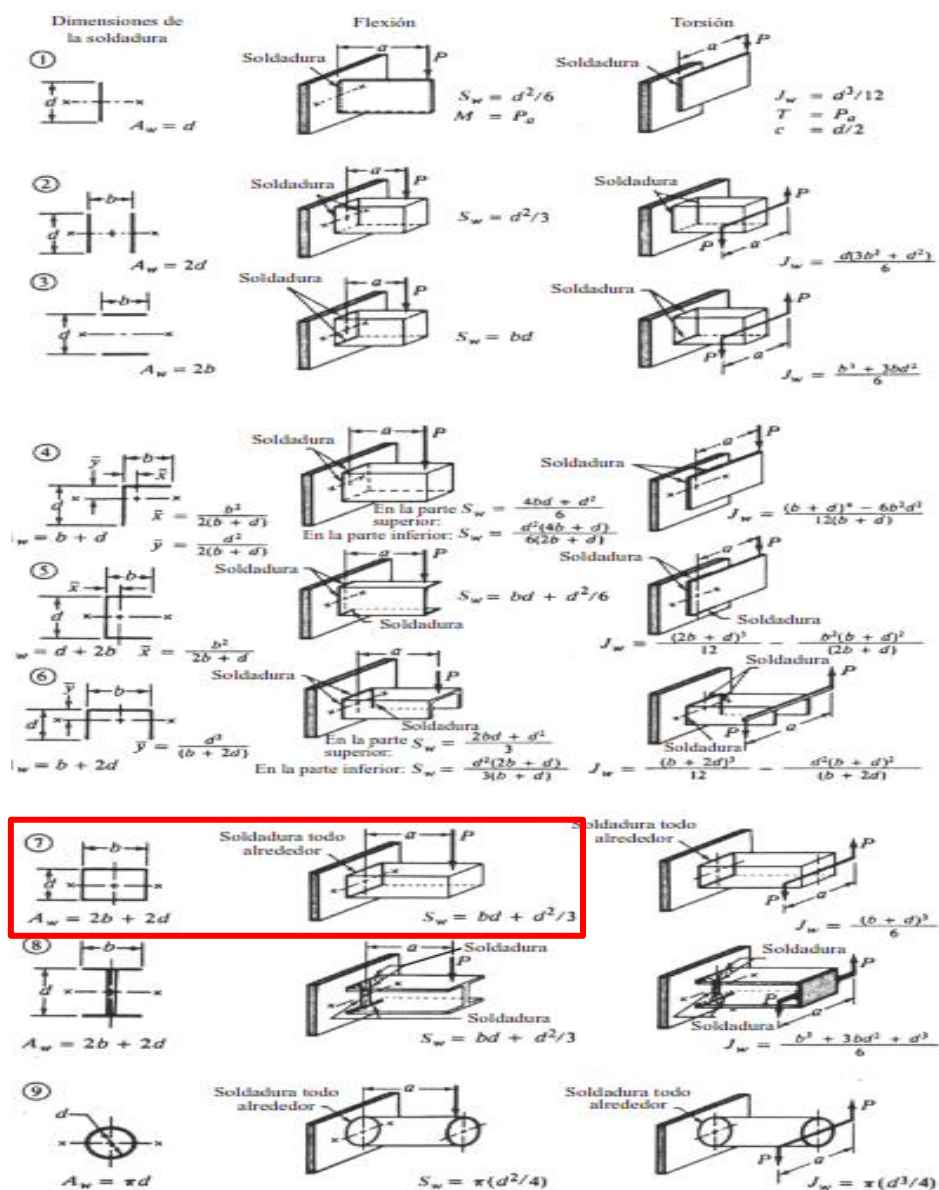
Factores geométricos para el análisis de soldadura [81].
